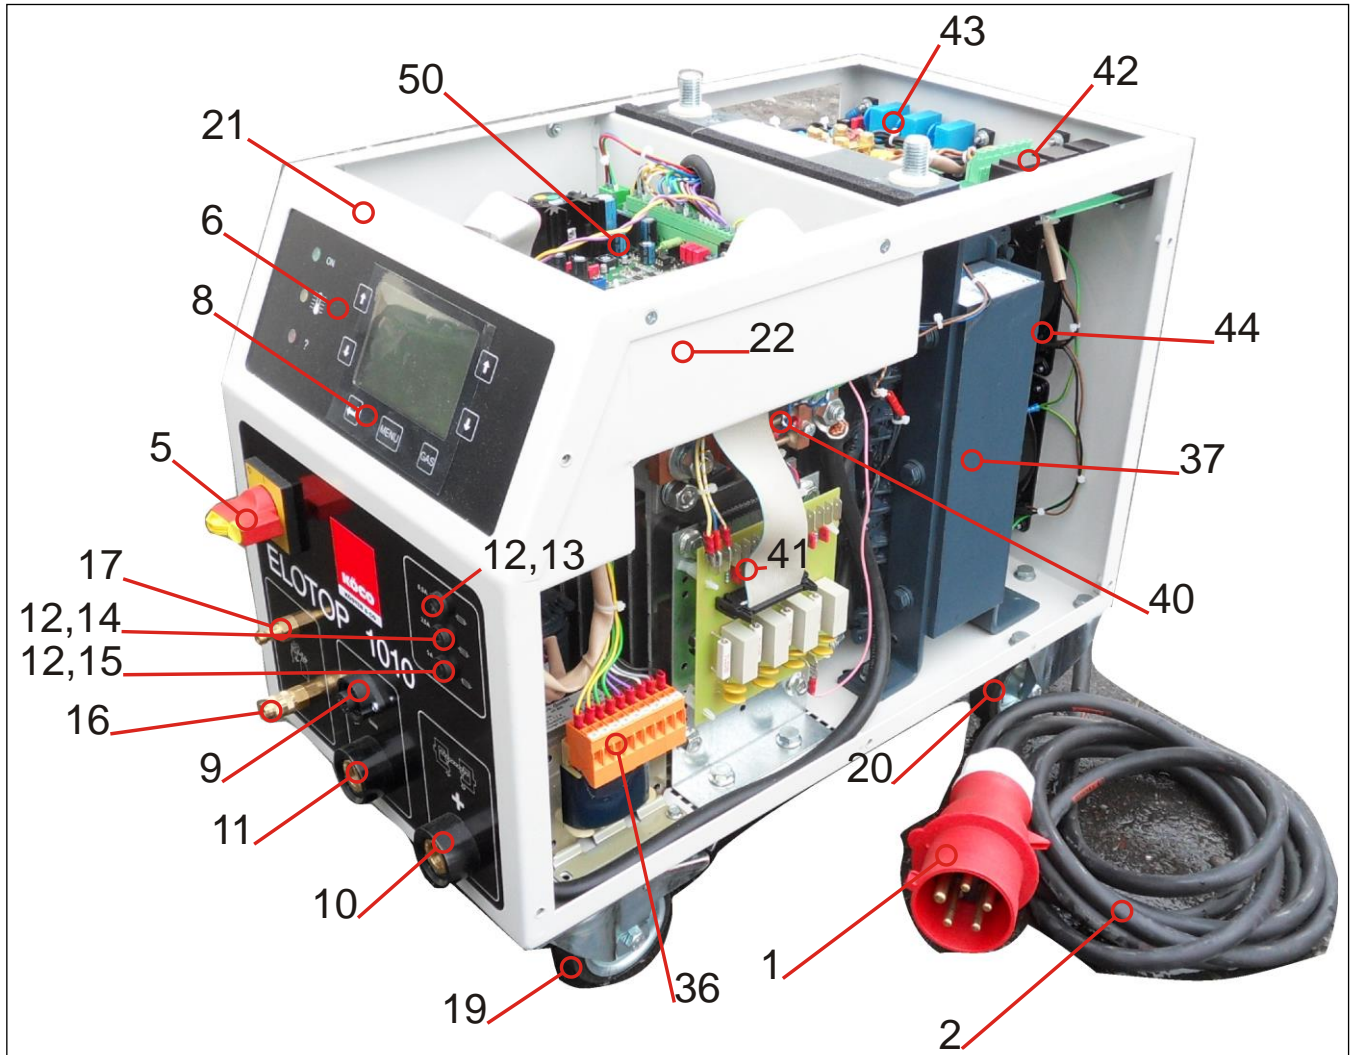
Front und Seitenansicht rechts ELOTOP 1010 (gilt auch für 810)
